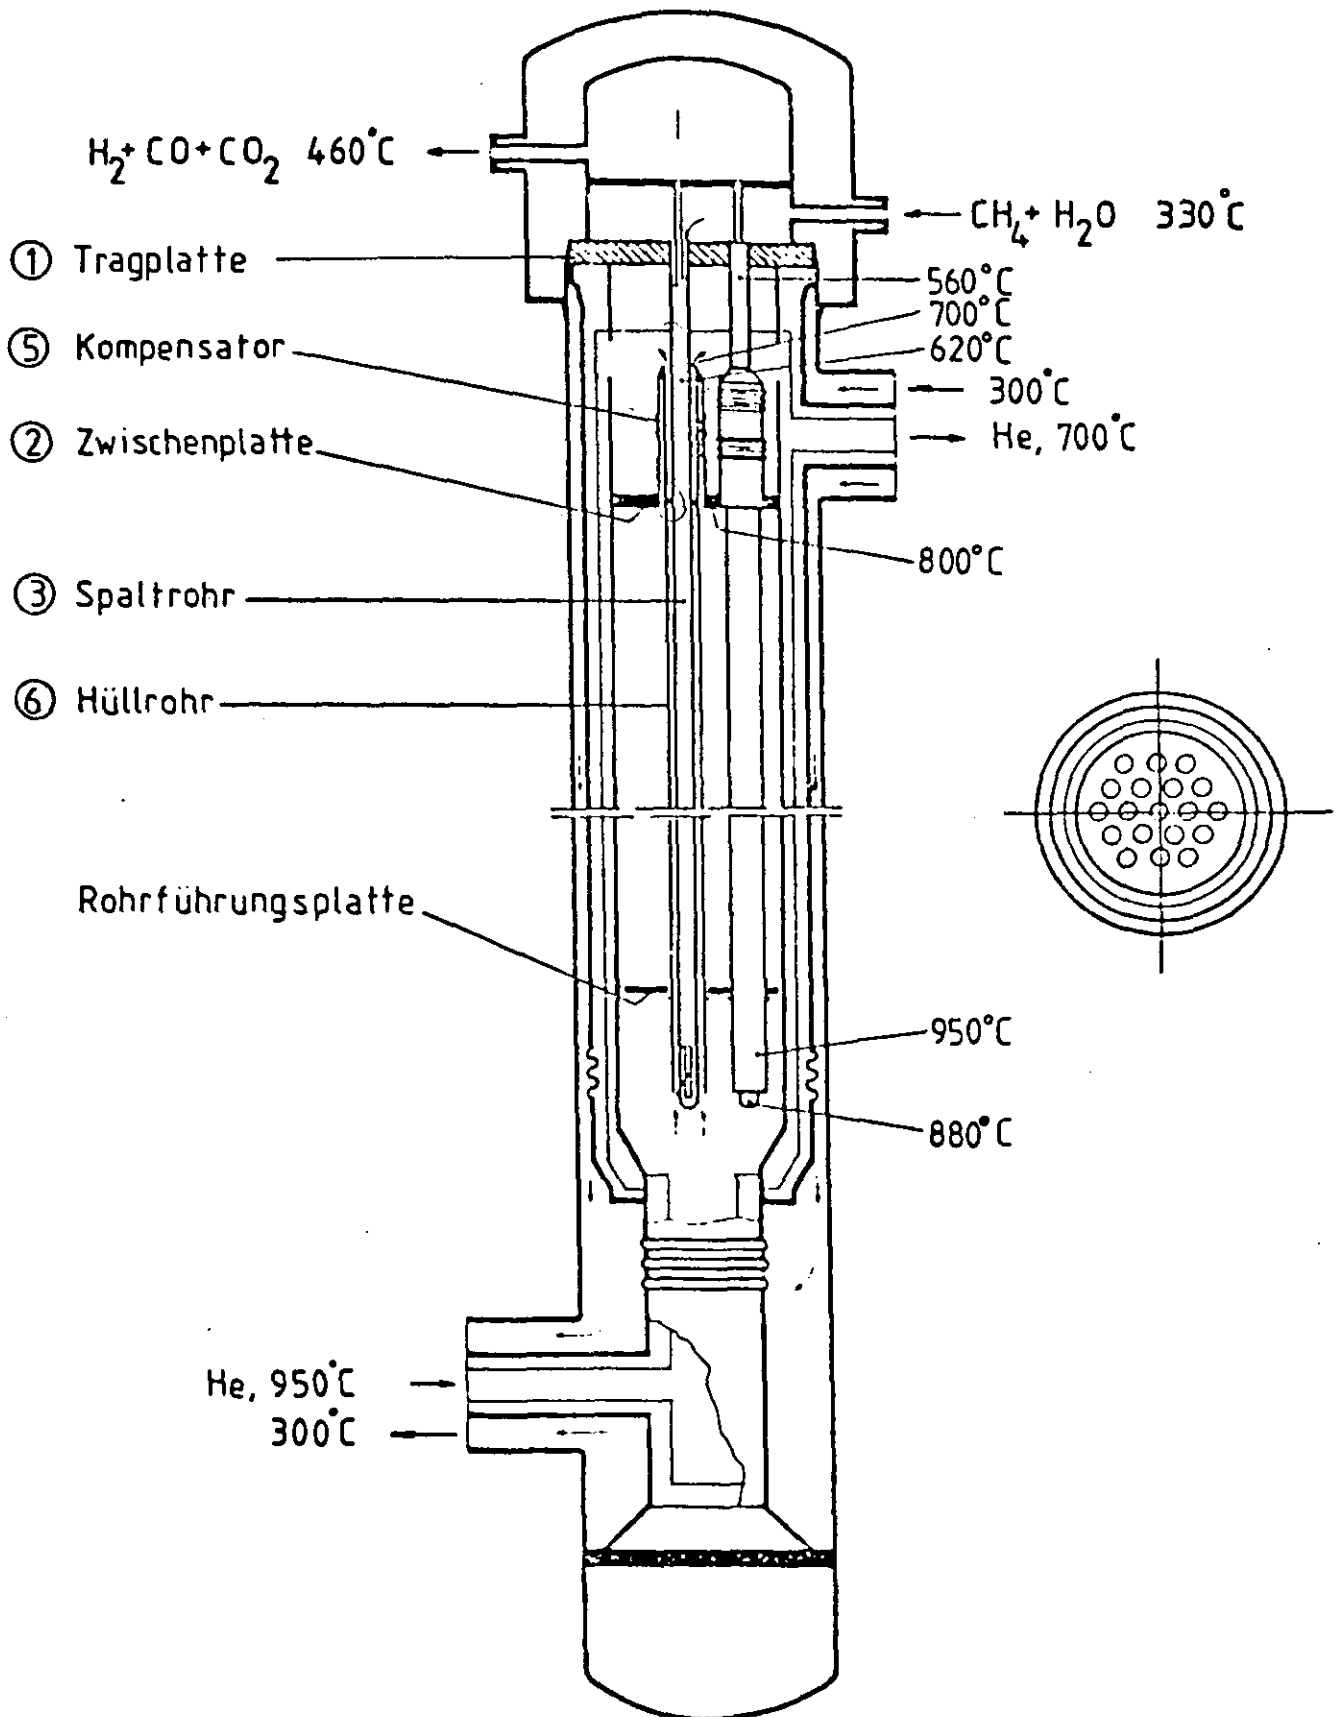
Konstruktiver Aufbau des Röhrenspaltofens mit Hüllrohr-gasführung
